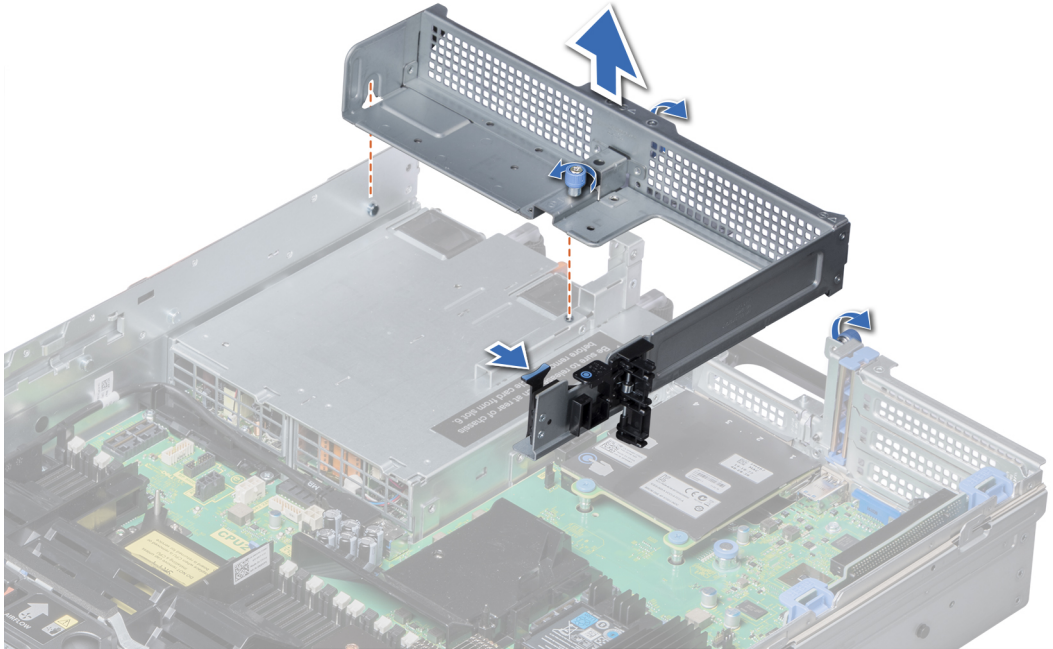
Entfernen der Platzhalter für Riser 2 und 3
